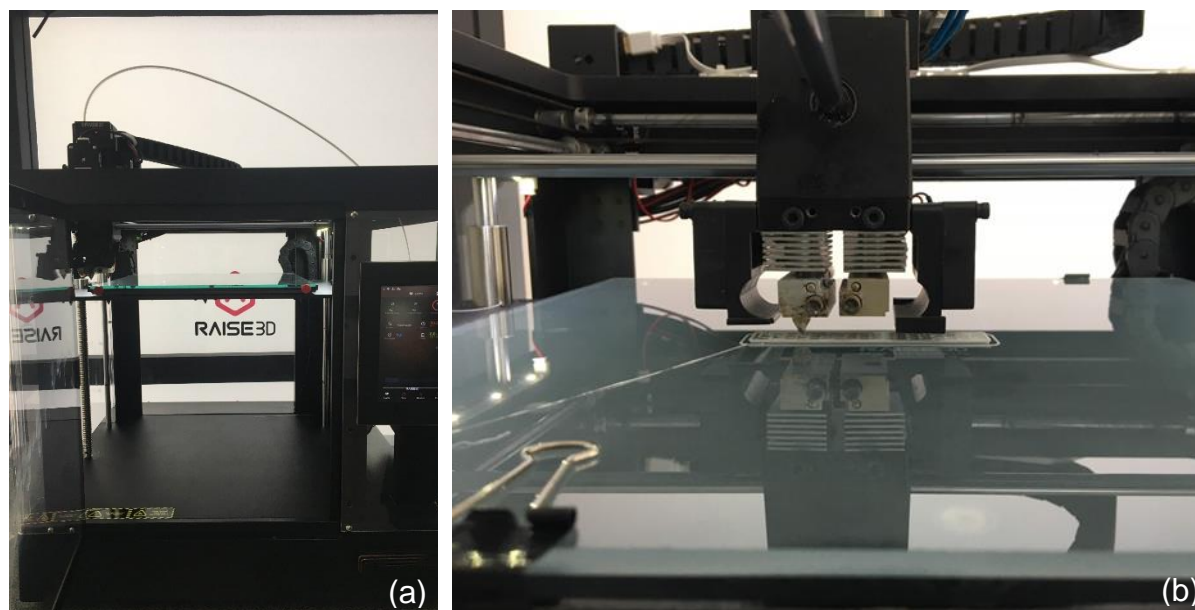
Impressora Raise 3D. (a) Impressora 3D e (b) bloco retangular sendo impresso.
